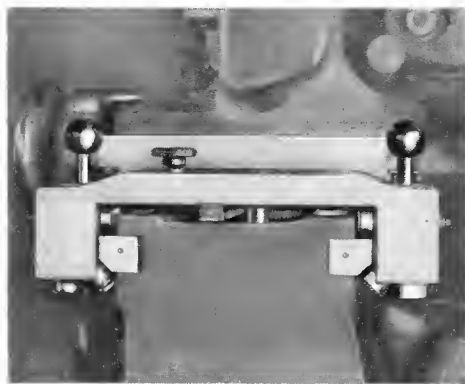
Schlittenführung an einer Innenschleifmaschine (Hess. Werkzeug- u. Apparatebau)
